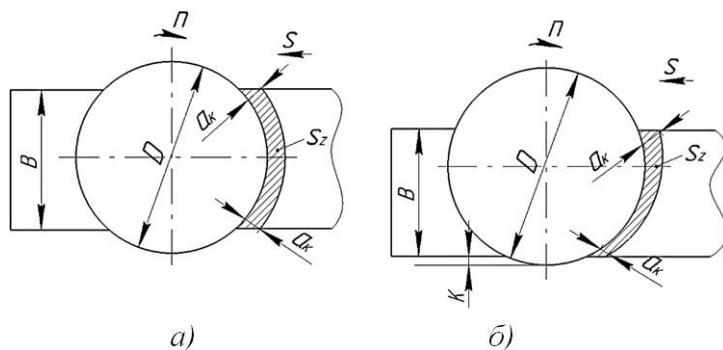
Схеми зняття припуску при фрезеруванні
